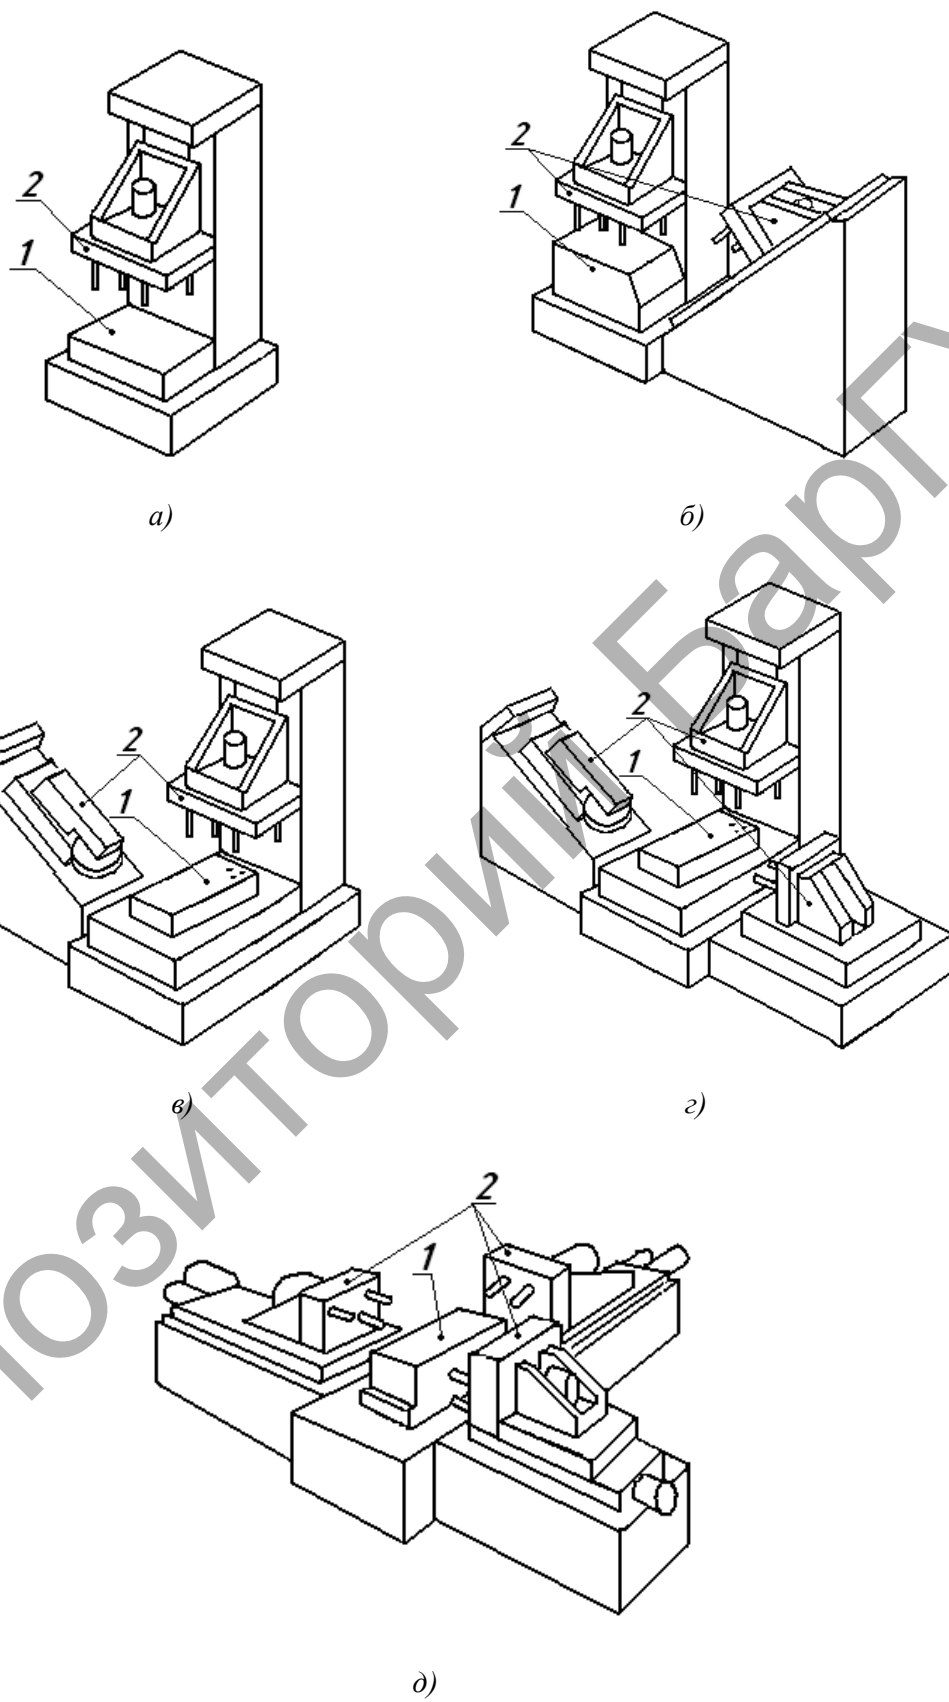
Типовые компоновки агрегатных станков со стационарными приспособлениями
